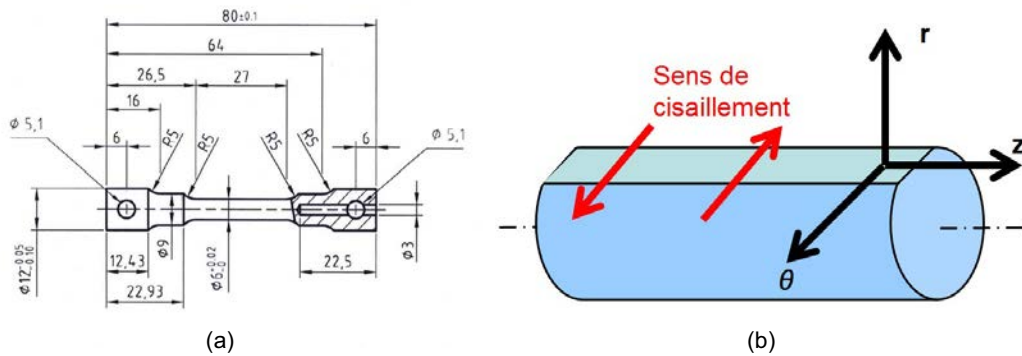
Éprouvettes de torsion. (a) Géométrie des éprouvettes de torsion (en millimètres). (b) Plan d'observation des éprouvettes de torsion.
